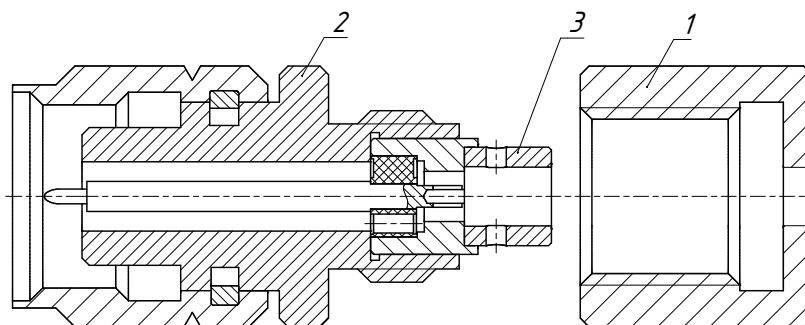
Кабельный соединитель ВК1-40-05-2 с отсоединенной стягивающей гайкой
